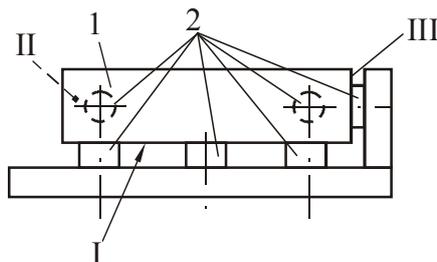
Схема установки призматической заготовки в приспособлении
